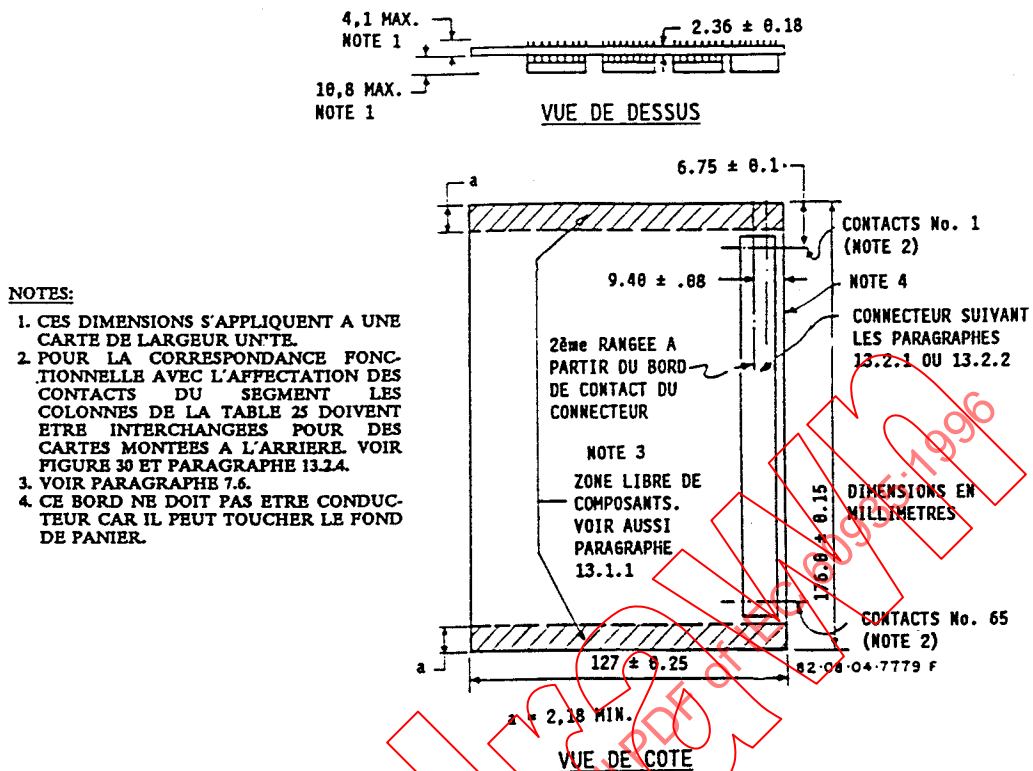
Circuit imprimé à monter à l'arrière du fond de panier
